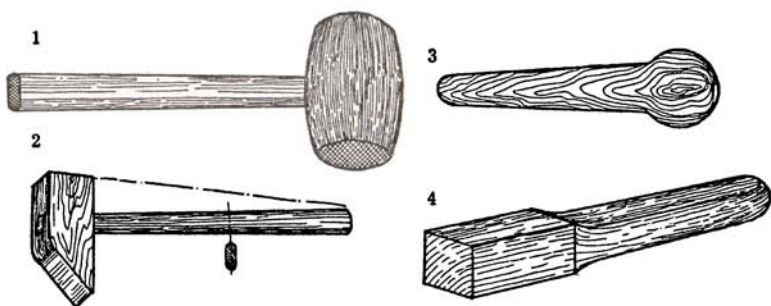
Киянки: 1 — киянка для маховых ударов; 2 — притирочный молоток; 3 — киянка со сферической головкой; 4 — киянка из бруса
